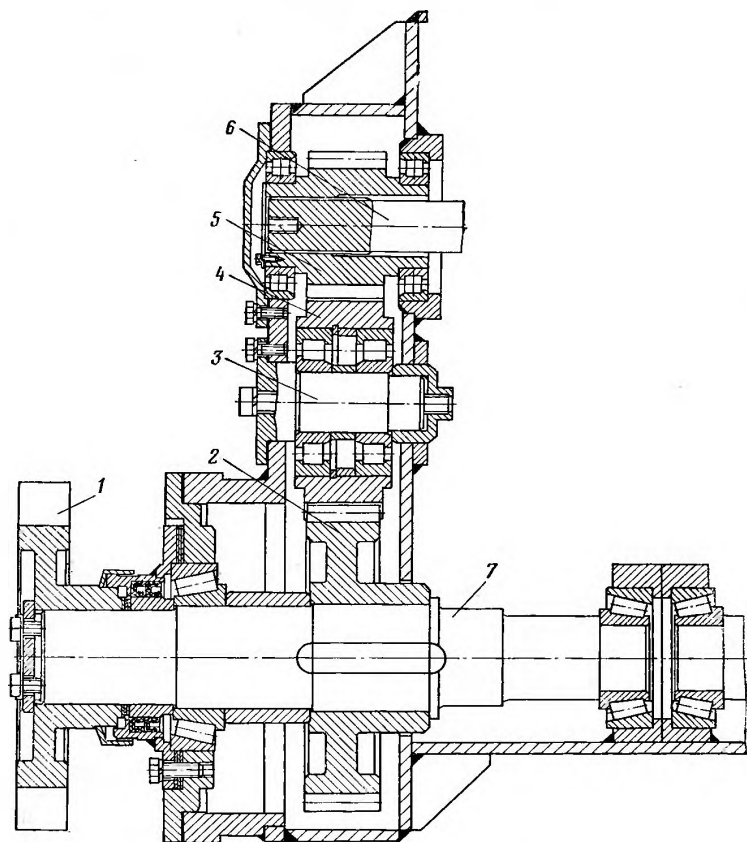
Редуктор и вал привода ротора экскаватора ЭТР231
